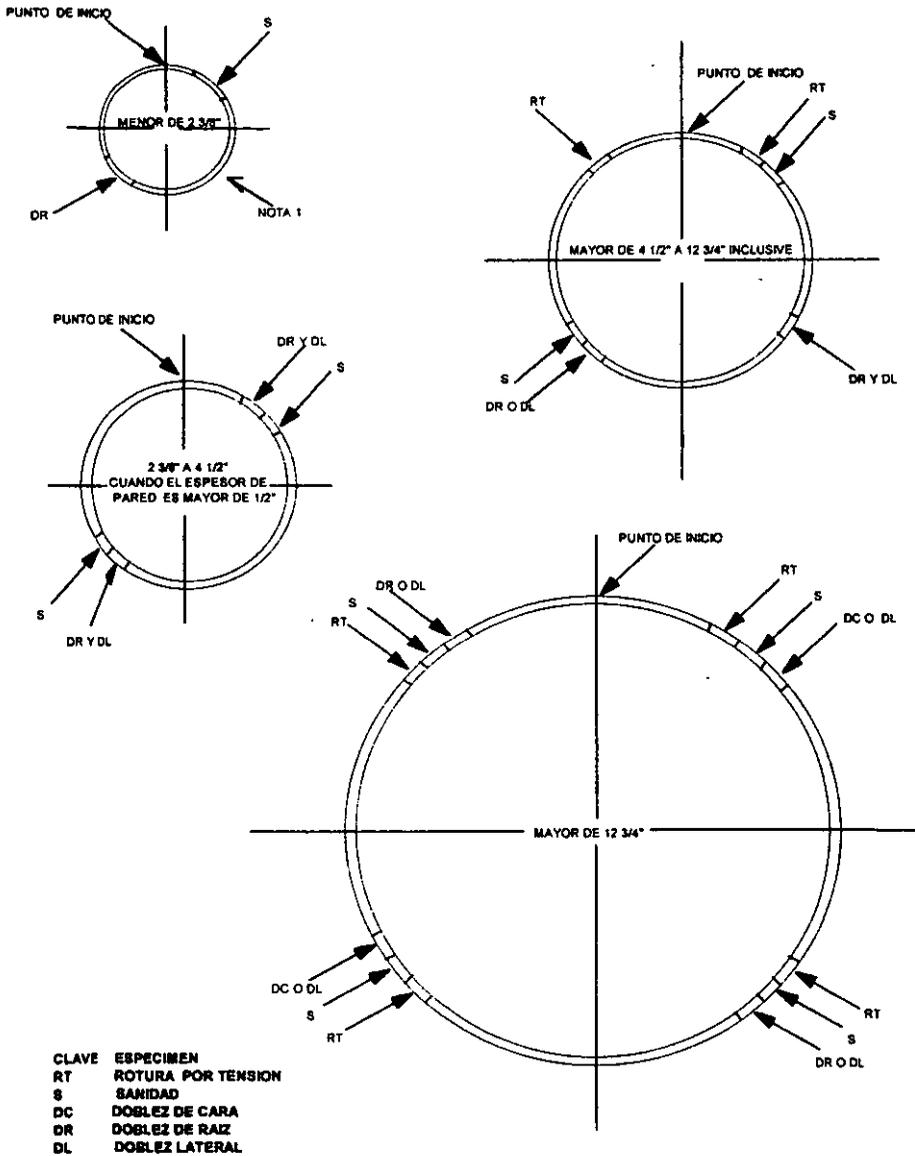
Localización de las Probetas para la Calificación de Soldadores en soldaduras a Tope
